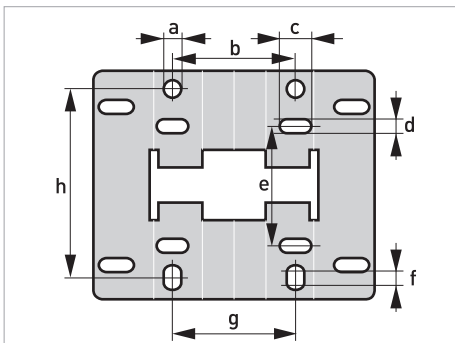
Размеры монтажной пластины корпуса для настенного монтажа
